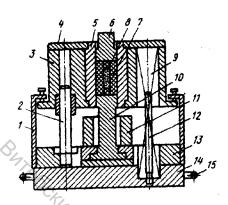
Устройство для изостатического формования в толстостенных эластичных оболочках 1 – ограничитель; 2 – направляющая втулка; 3 – обойма; 4 – крышка; 5 – матрица; 6 – верхний пуансон; 7 – толстостенная оболочка; 8 – прессуемый порошок; 9 – пружина; 10 – нижний пуансон; 11 – вилка; 12 – стержень; 13 – верхняя плита; 14 – нижняя плита; 15 – ручка
